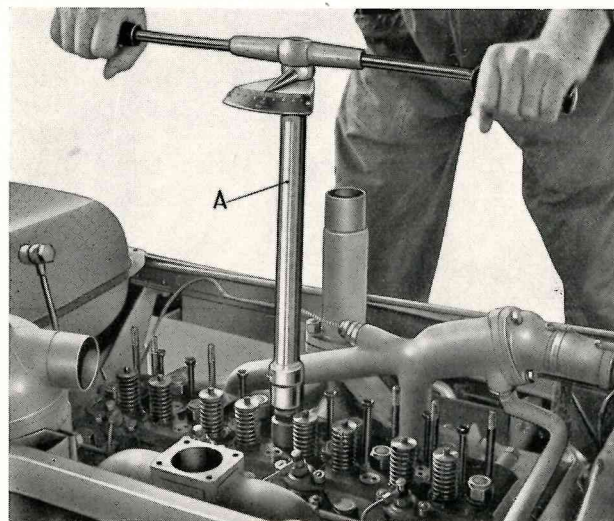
Serraggio dei dadi fissaggio testa cilindri. A, Chiave dinamometrica.
